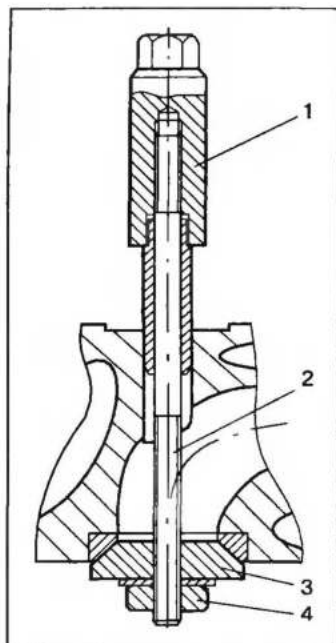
Запрессовка направляющей втулки с помощью винтового приспособления с опорой и центрированием по седлу клапана: 1 — толкатель; 2 — шпилька; 3 — опорная шайба; 4 — гайка
